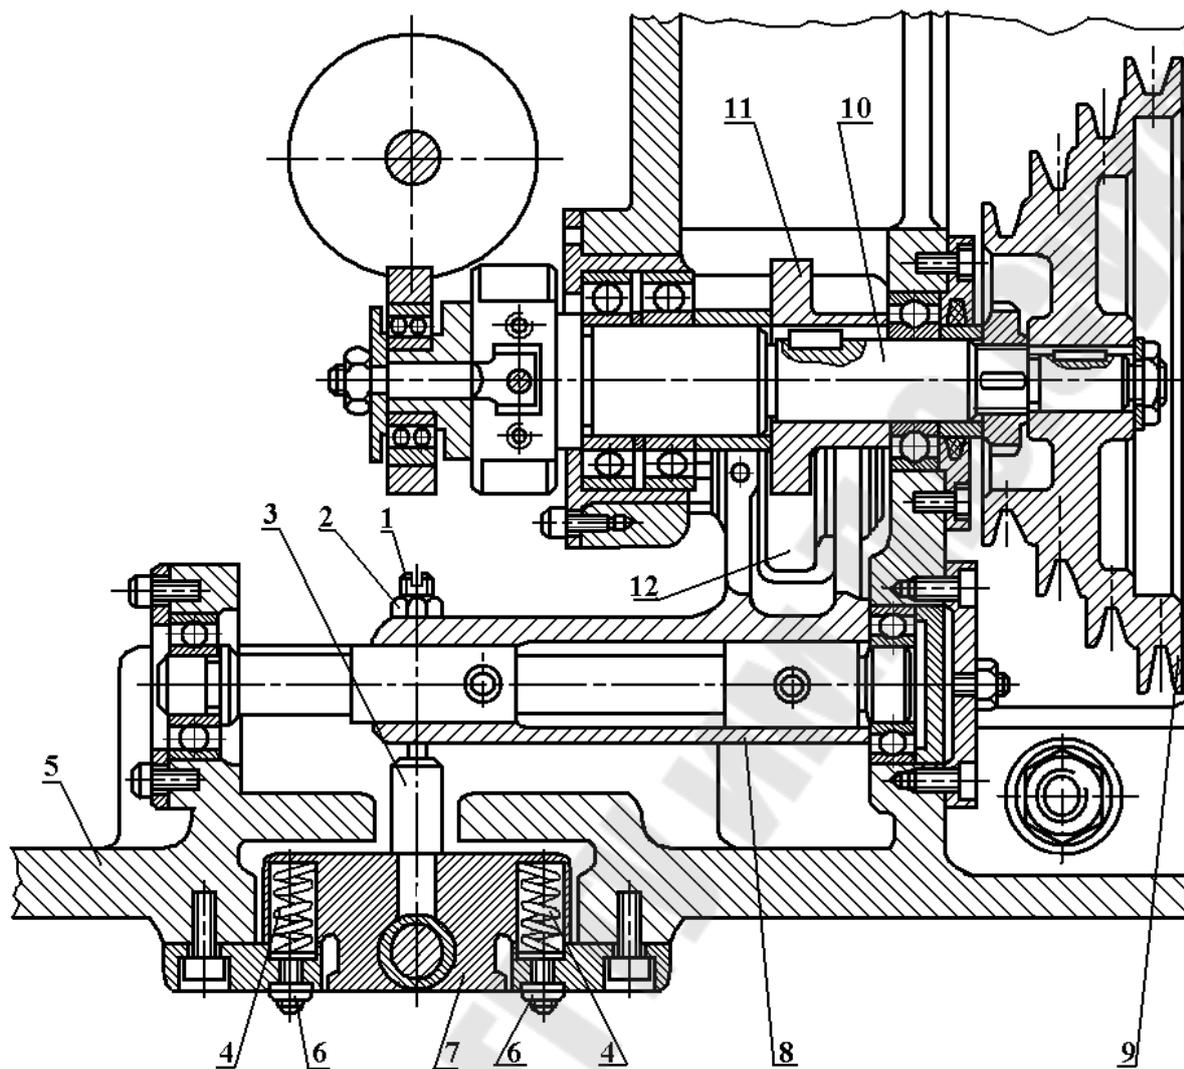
Эскиз механизма отвода долбяка от заготовки
